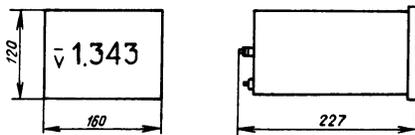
Габаритный чертеж приборов типов Ф294, Ф295, Ф296, Ф298, Ф299
